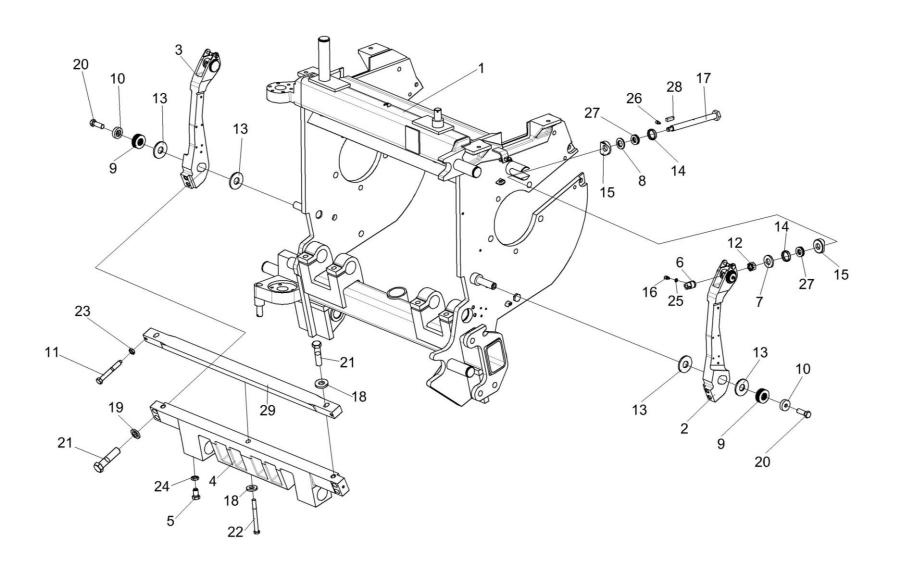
Установка рычагов КВК 0115170 и КВК 0115170-01
